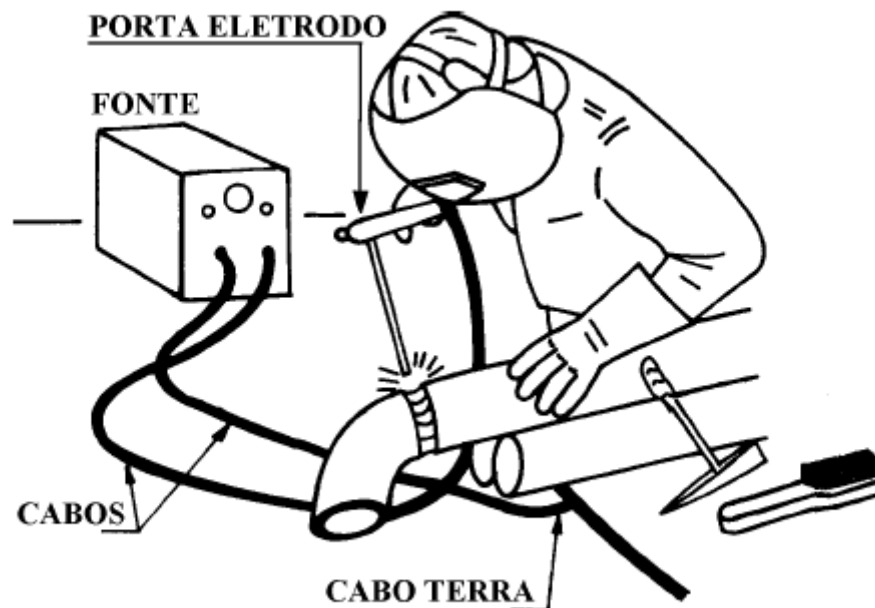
Equipamento para a soldagem com eletrodo revestido
